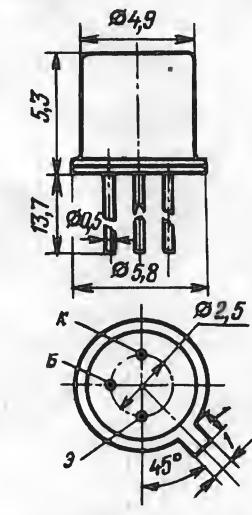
Чертеж корпуса и цоколевка транзисторов серии КТ3102
